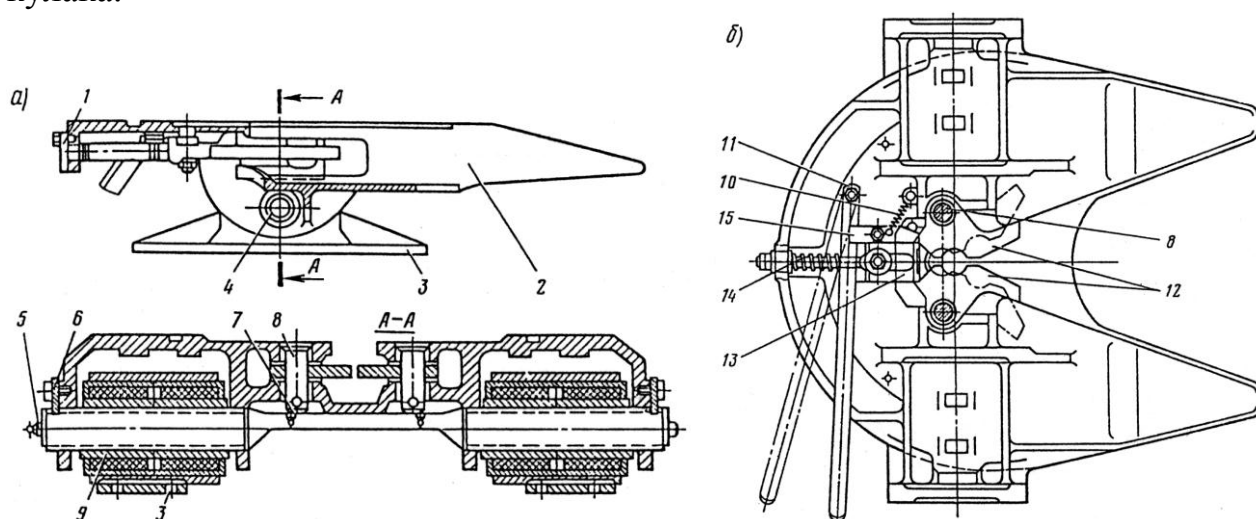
Седельно-сцепное устройство автомобиля-тягача МАЗ-504В:
